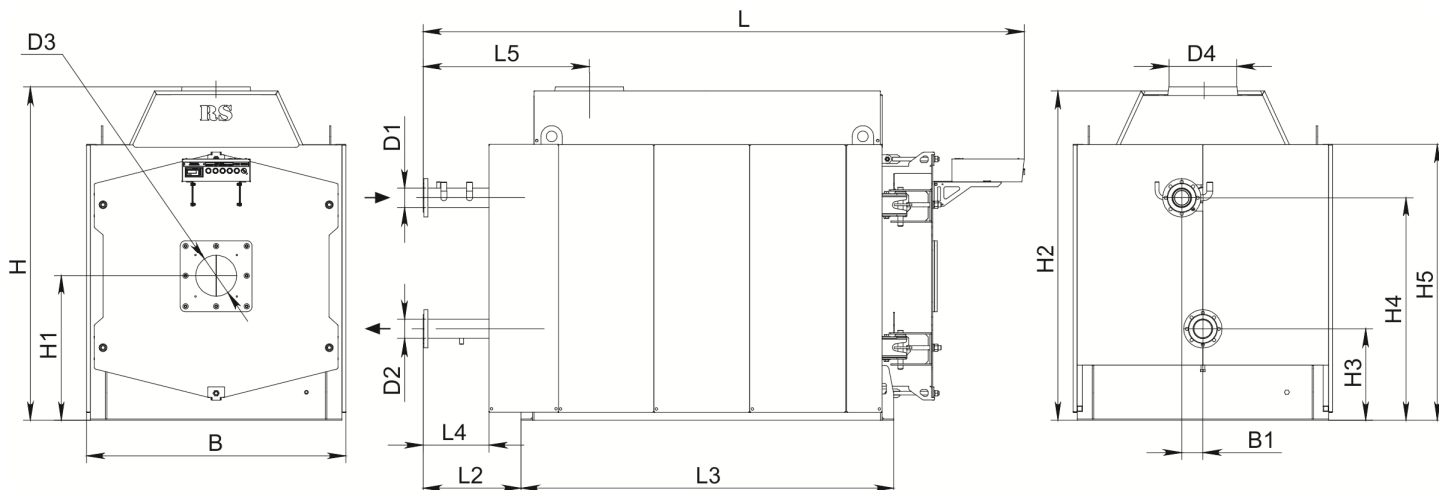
Габаритные и присоединительные размеры котлов RS-D800, RS-D1000
